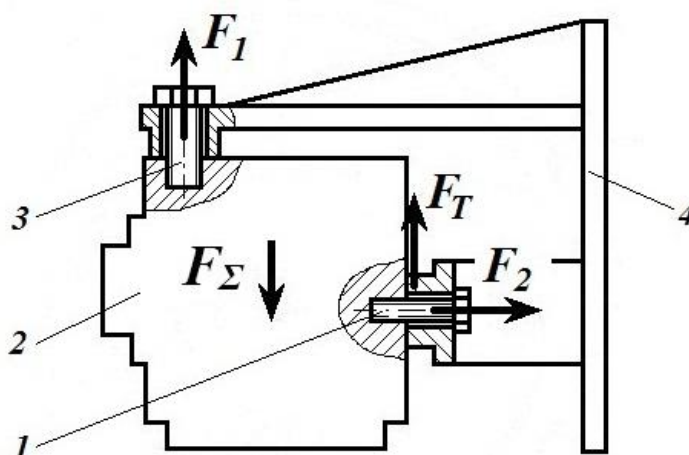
Схема закрепления агрегата на адаптере с помощью резьбовых элементов самого агрегата
